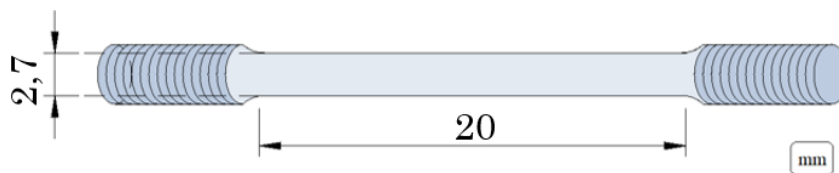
de las probetas cilíndricas para ensayos de tracción simple, orientadas paralelamente al eje longitudinal de las barras
